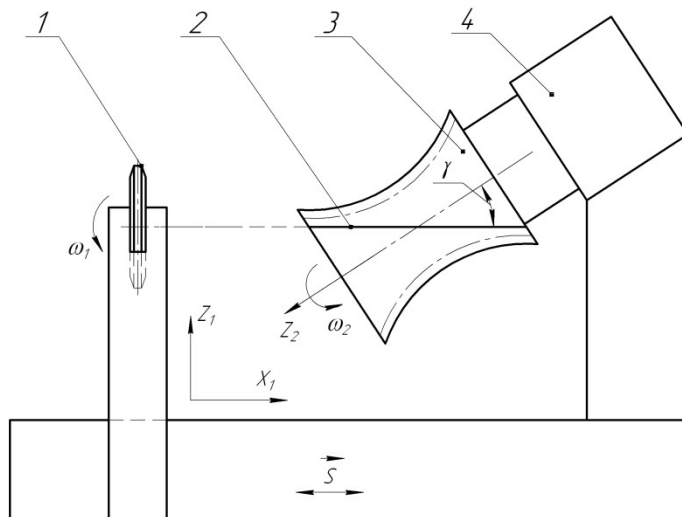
Схема формообразования витков шлифовального круга на поверхности однополостных гиперboloид прямобочным роликом: 1 – прямобочный ролик; 2 – прямолинейная образующая винтовой гиперboloидной поверхности; 3 – гиперboloидная заготовка шлифовального круга; 4 – делительная головка
